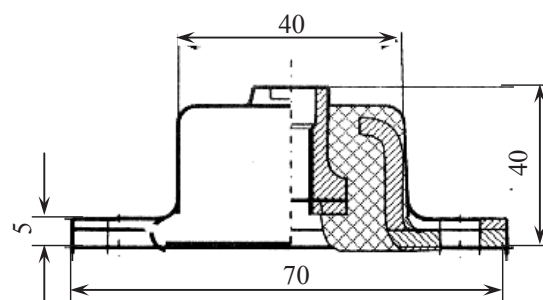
Базова конструкція гумометалевого амортизатора АКСС-10 М
